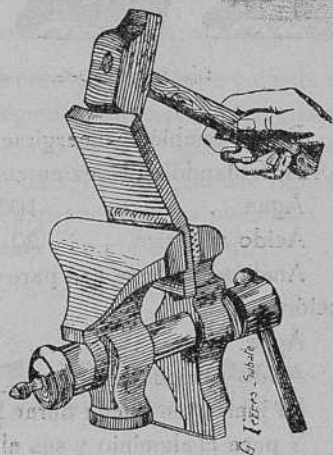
Ensayo de una soldadura doblándola por la cara posterior.
